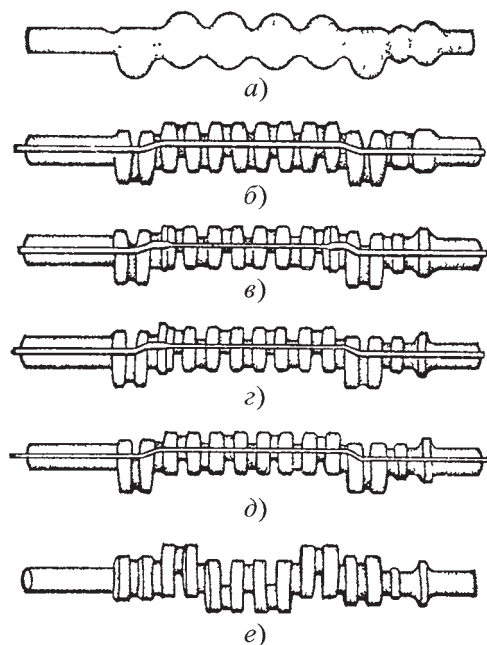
Переходы штамповки коленчатого вала: а — заготовка после штамповки в заготовительном штампе; б–д — штамповка в секционном штампе; е — обрезка облой в обрезном штампе
